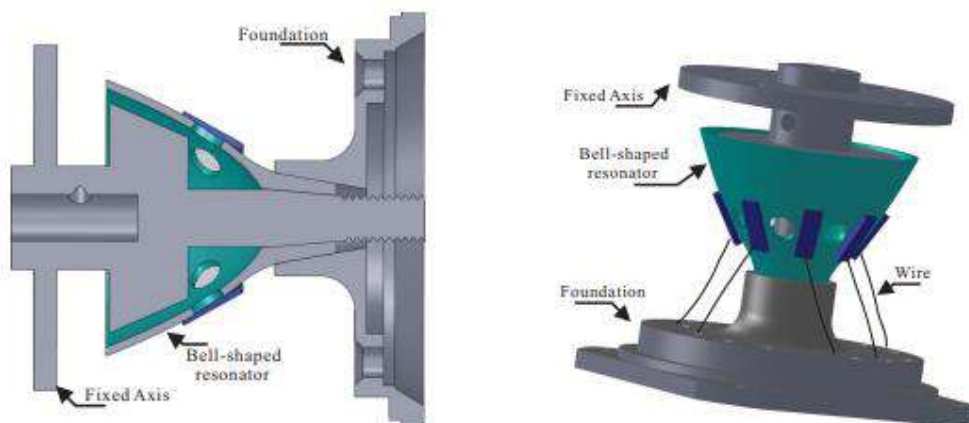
3D вид конструкции колоколообразного ВТГ
